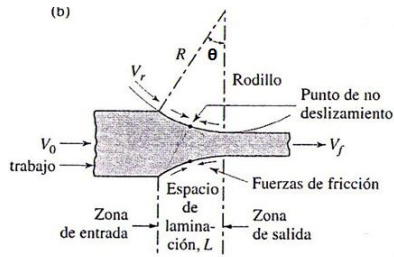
Fuerzas que actúan sobre la superficie del rodillo.
